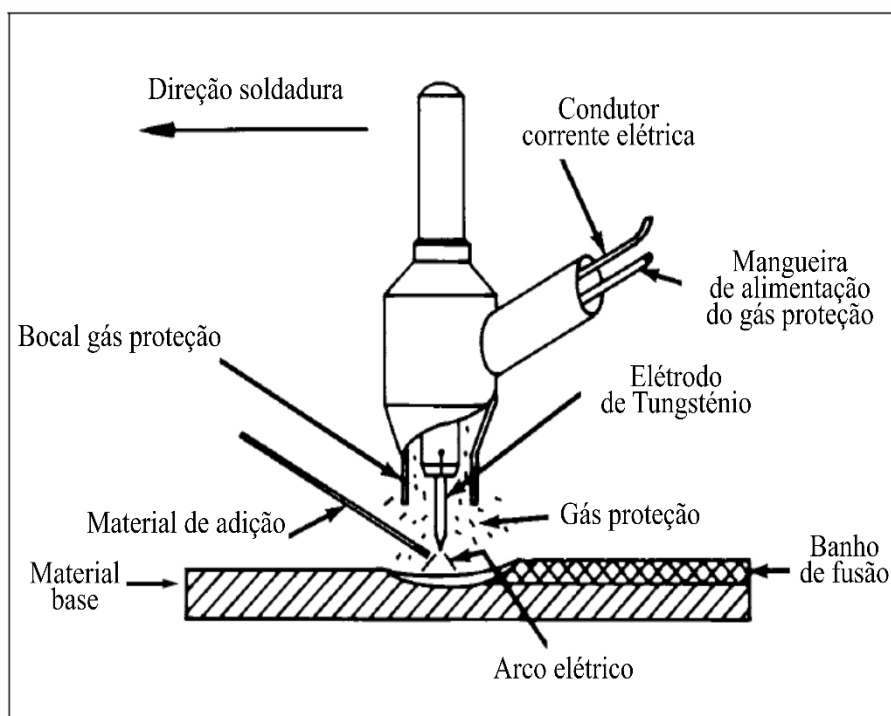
Esquema do processo de soldadura TIG, adaptado de [6].
